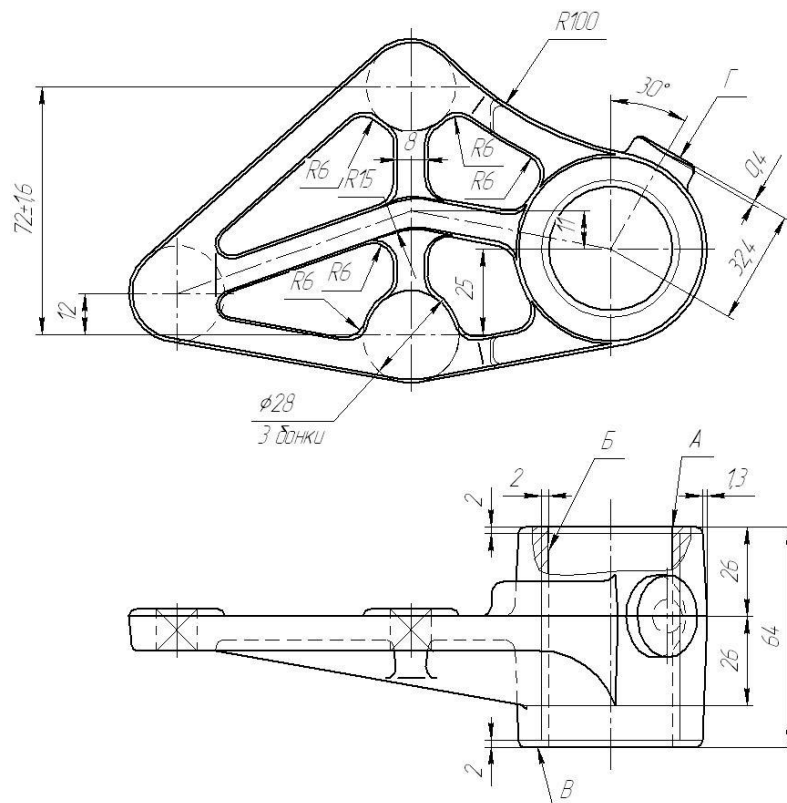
Підшипник з нанесеними припусками на механічну обробку
